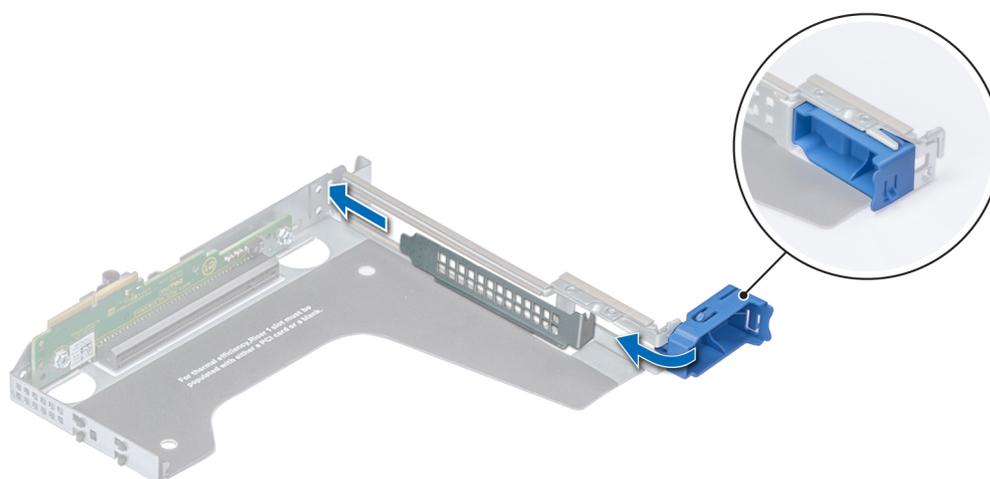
Installation de la plaque de recouvrement pour la carte de montage 1
